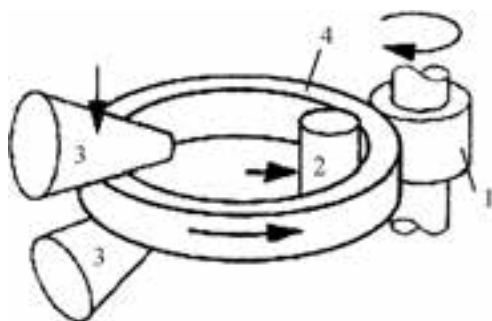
Радиально-осевая кольцераскатка: 1 — осевые валки; 2 — кольцо; 3 — дорновой валок; 4 — главный валок
